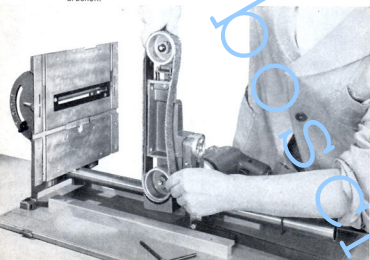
Befestigen des Bandschleifarms mit angebauter Maschine im Maschinenhalter.
